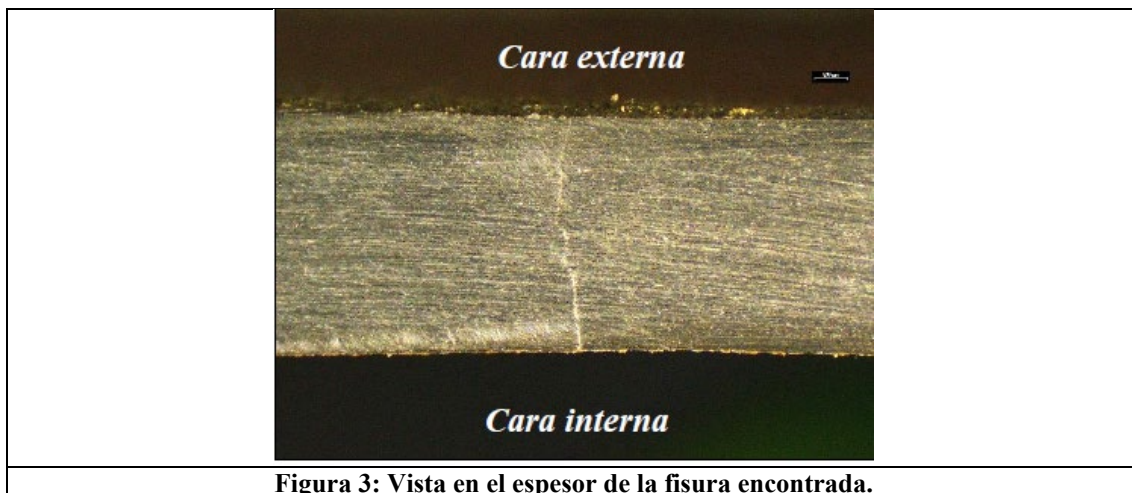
Vista en el espesor de la fisura encontrada.
